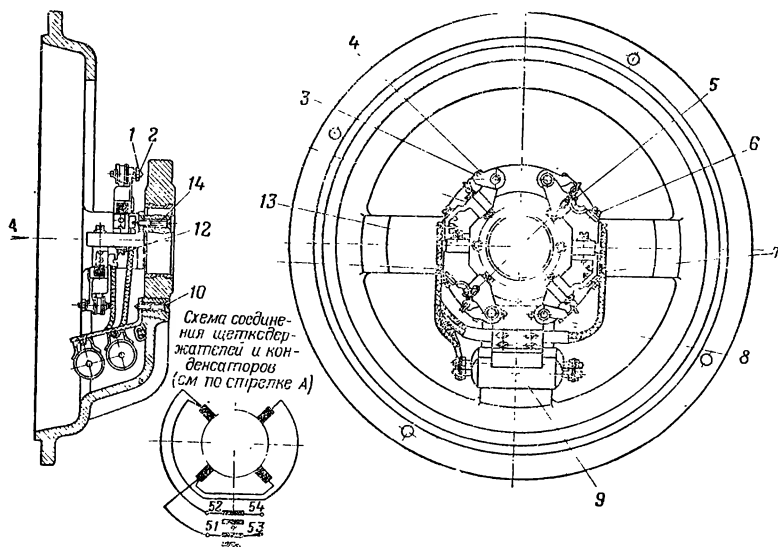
Подшипниковый щит генератора ГАБ-8-Т/230 со стороны контактных колец:
